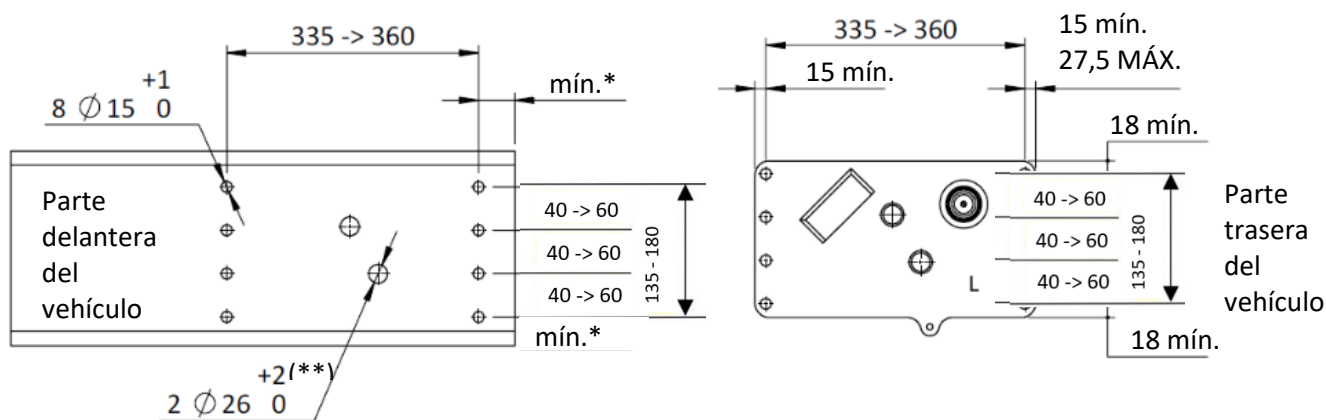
Plano de montaje autorizado para la pletina baja no perforada
